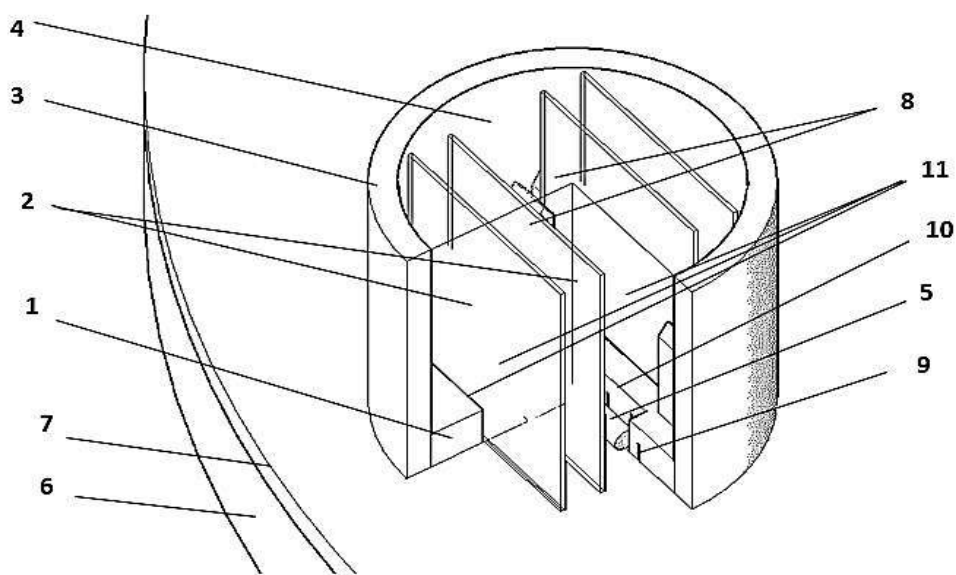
Фиксатор образцов картона: *1* – основание; *2* – образцы; *3* – заливочная форма; *4* – синтетический полимер; *5* – калибровочный элемент; *6* – основание шлифовально-полировального станка; *7* – абразивное покрытие; *8* – направляющие; *9* – размерная шкала; *10* – прямоугольное отверстие для калибровочного элемента; *11* – фиксаторы-зазоры [152]
